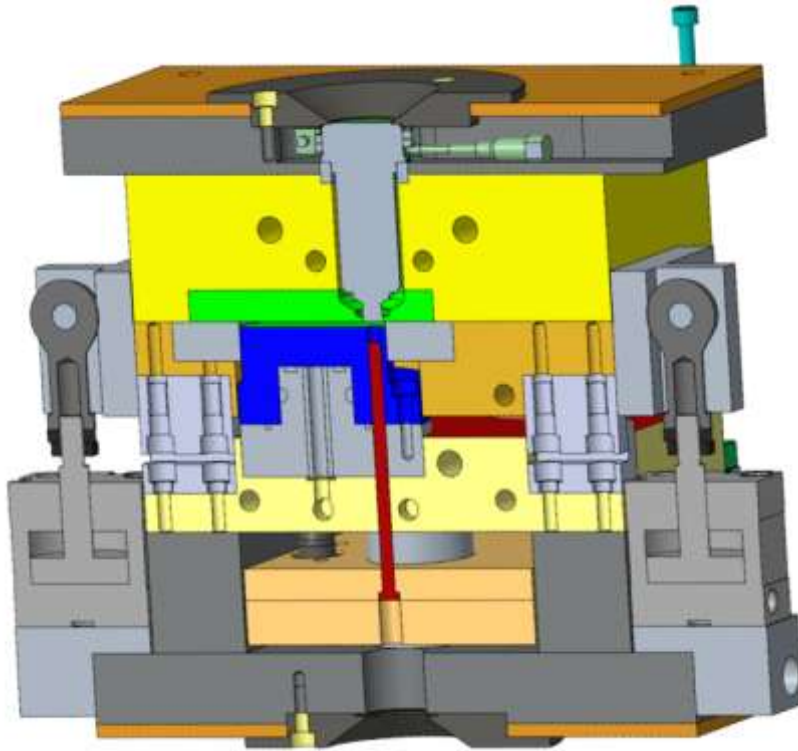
Spritzprägewerkzeug für LDS-MID
